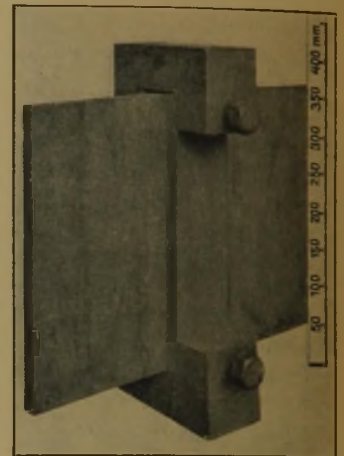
Einspannschweißprobe nach T. Wilkinson und H. O'Neill (L.M.S.-Versuch).
